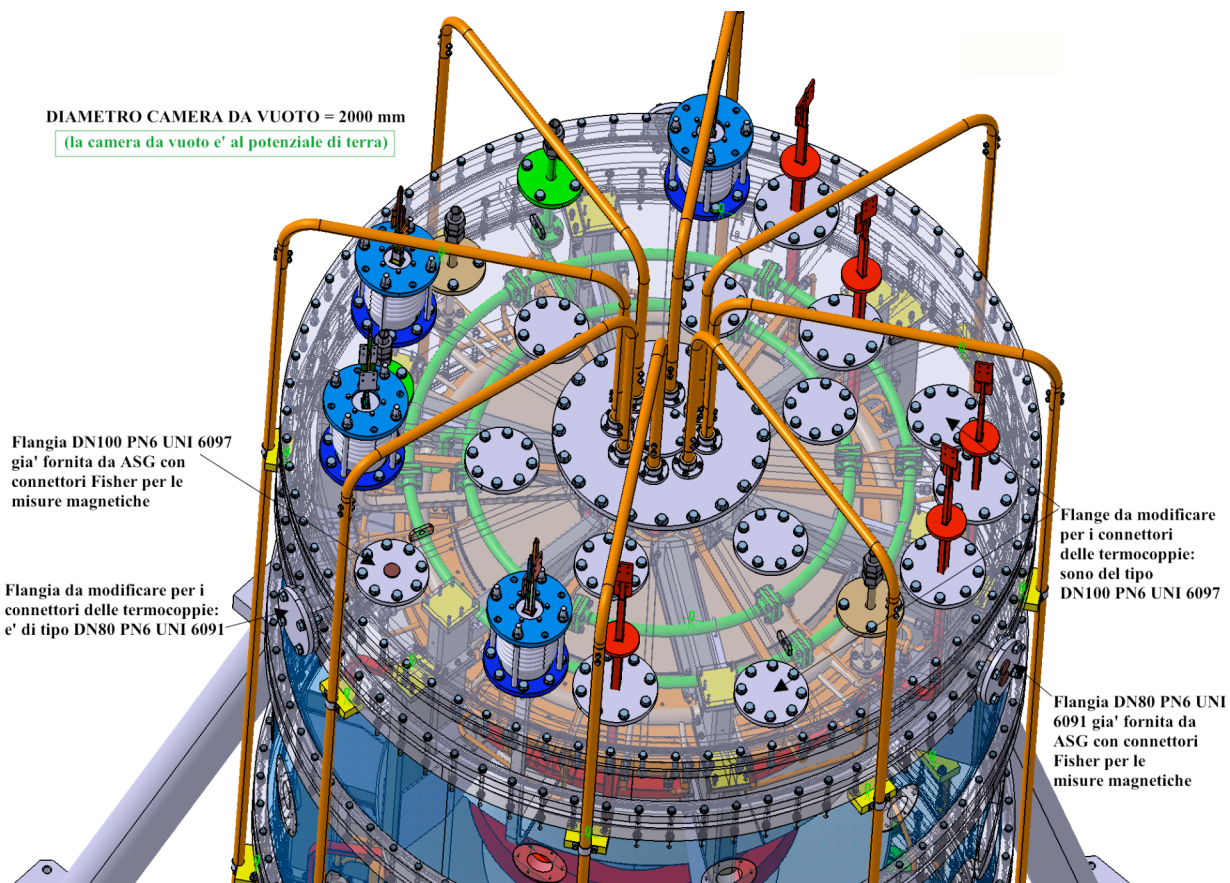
Parte superiore del Load Assembly di Multi-Pinch/PROTO-SPHERA
